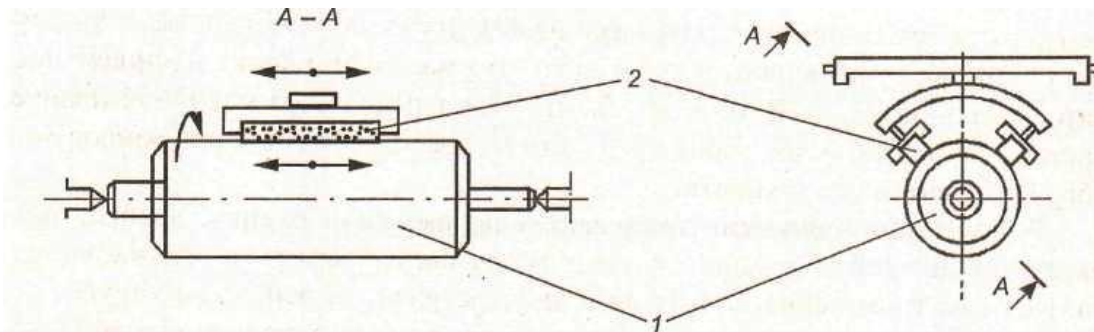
Схемы движений заготовки и инструмента при суперфинишировании: 1 -заготовка; 2 – инструмент.
